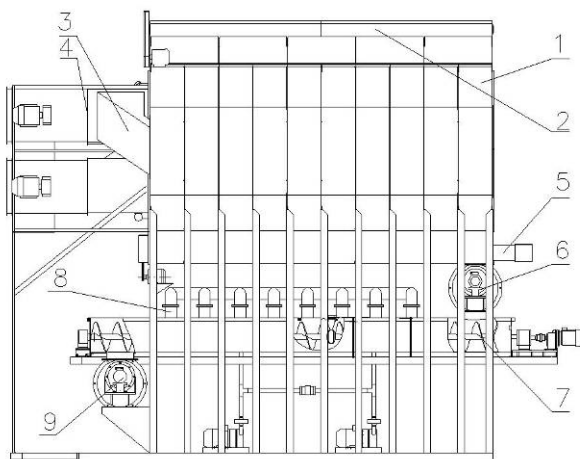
Схема установки для сушки и вакуумного охлаждения зерна (главный вид)
